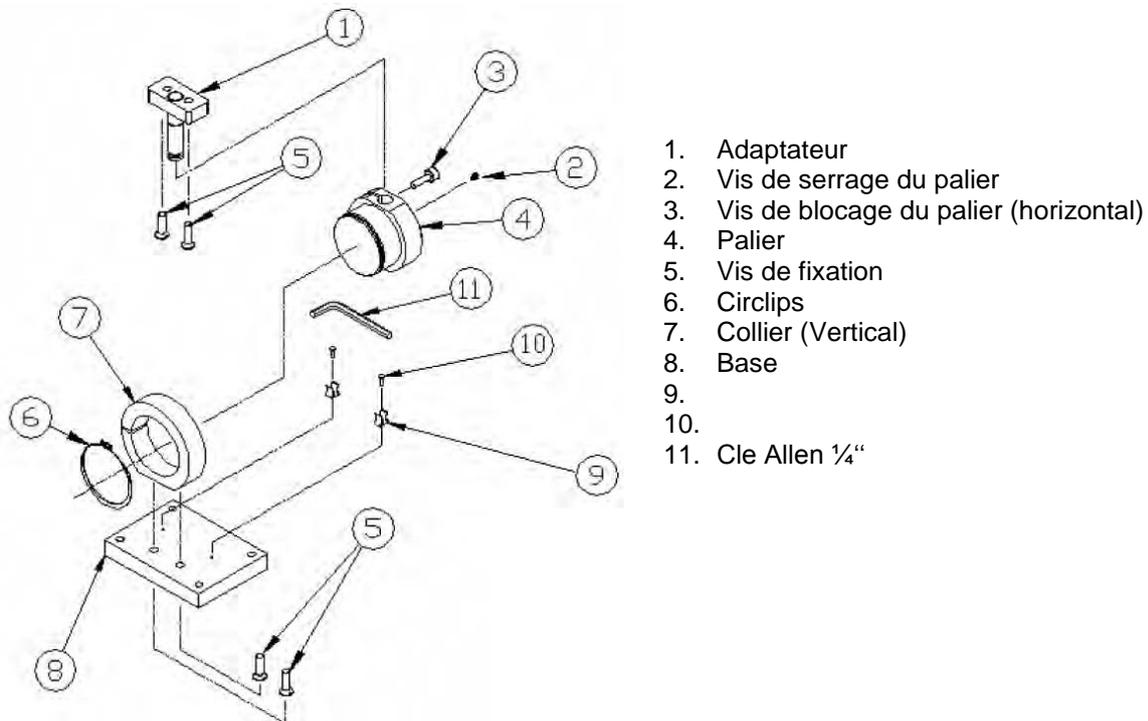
Vue éclatée de la base de montage réglable (E-MB)
